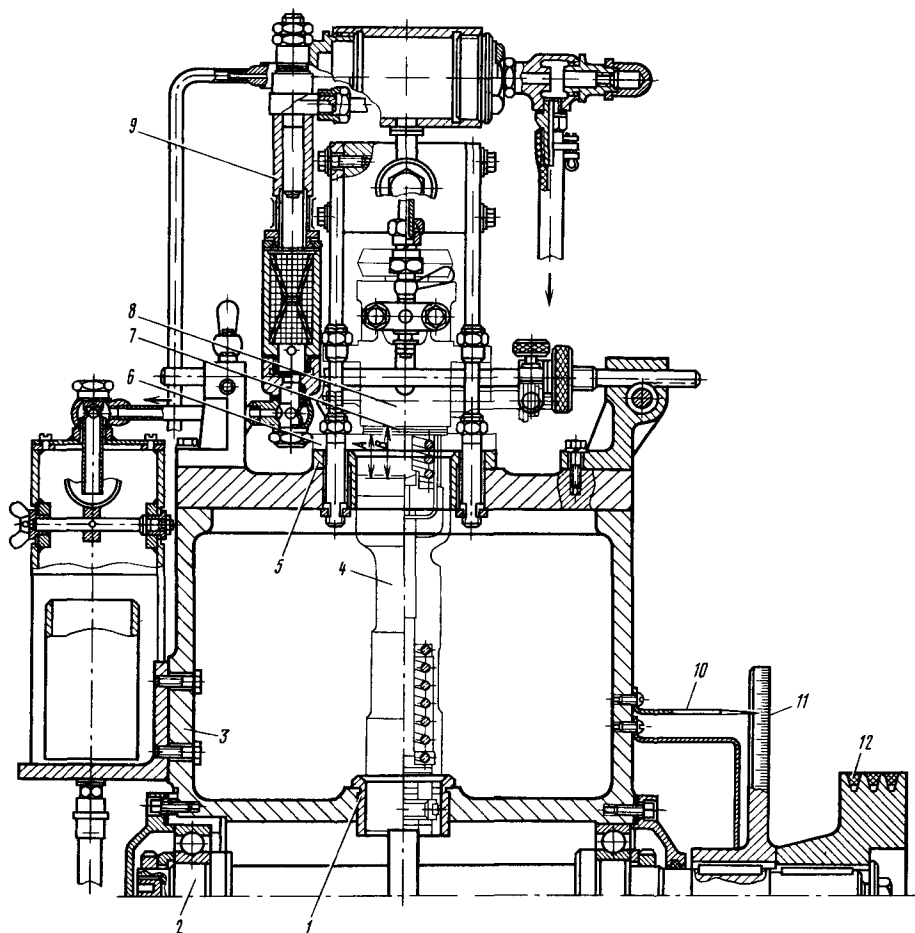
Стенд для обкатки, испытания и регулировки топливного насоса дин2Д100
